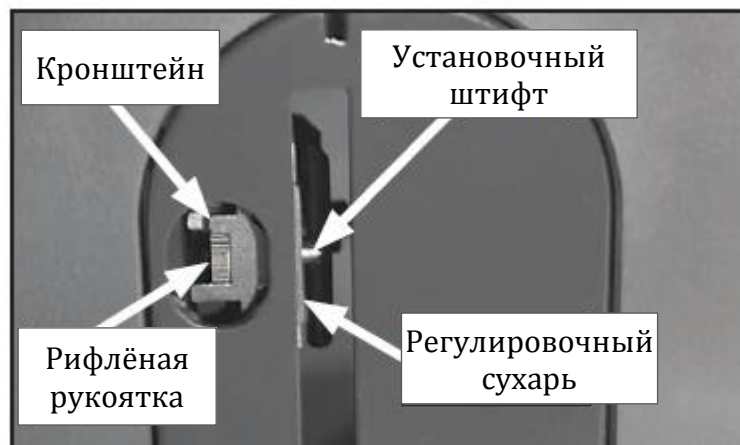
Рифлёная рукоятка, используемая для крепления распорки
